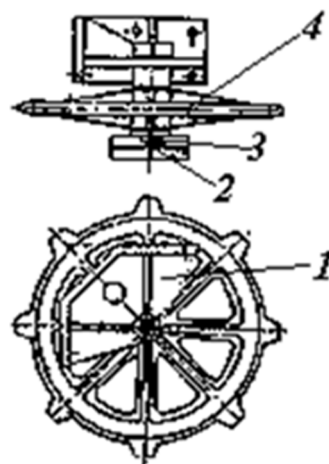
Обертова станція робочої ділянки конвєсера з пальцем знизу:
